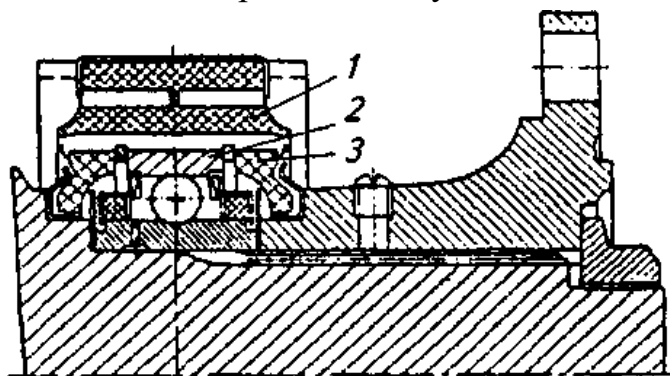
Промежуточная опора карданной передачи: 1 — упругий элемент; 2 — опорный шарикоподшипник; 3 — защитное уплотнение
